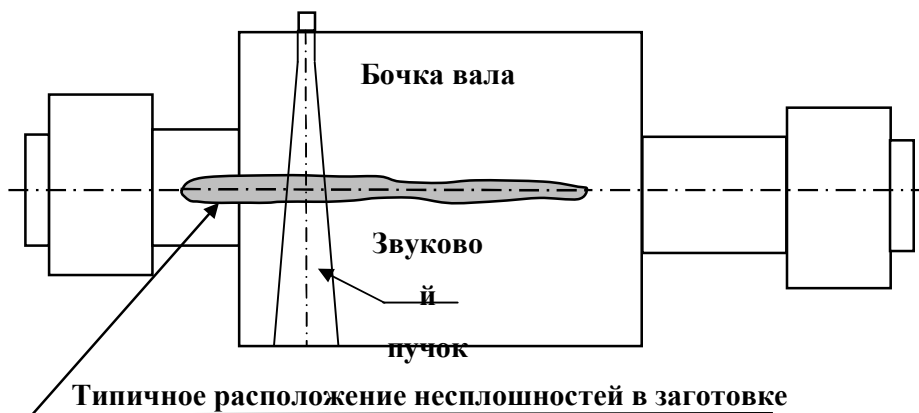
Типичные форма заготовки вала и область расположения несплошностей
